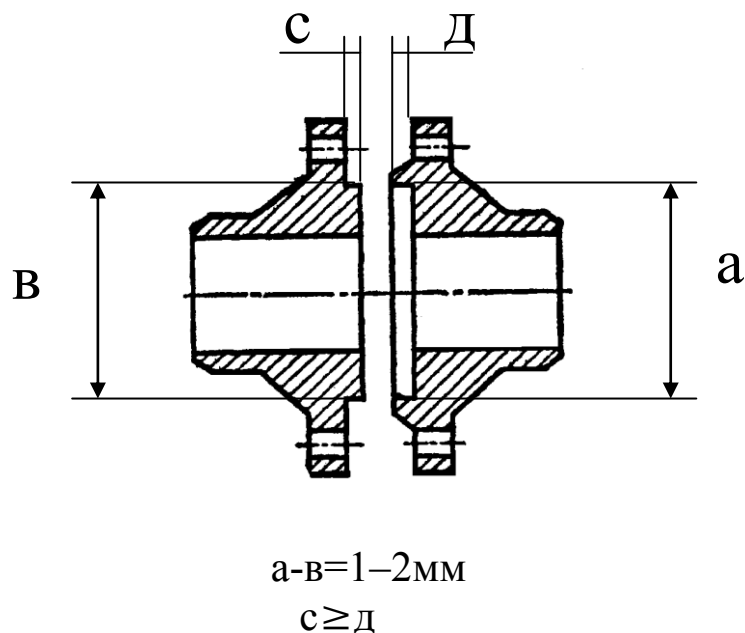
Допуски размеров "выступ"- "впадина"
